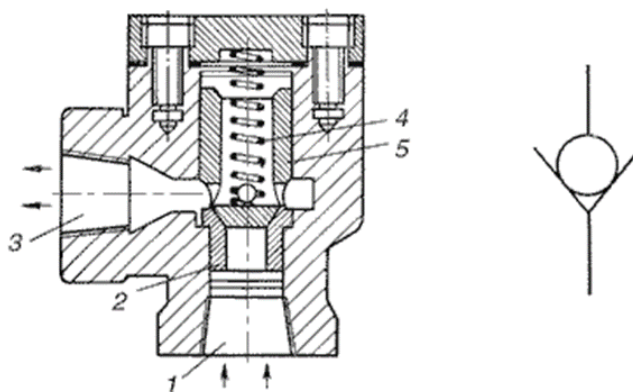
Конструкция и условное обозначение обратного гидроклапана
